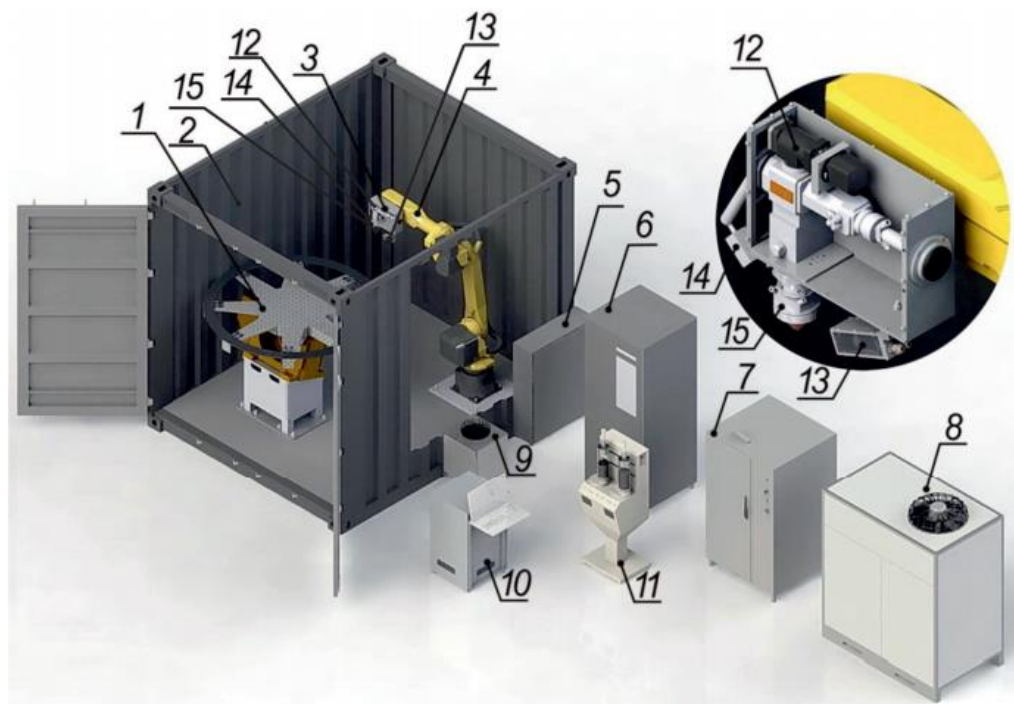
Загальна схема обладнання для реалізації технологій лазерного наплавлення: 1–Двох координатний стіл; 2–Робоча камера; 3–Лазерна голова; 4–робото технічний маніпулятор; 5– Вузол підготовки та подачі газової суміші; 6–пристрій очищення та сушіння газу; 7– Волоконний лазер; 8–Охолоджувач; 9–система охолодження; 10–Пульти управління; 11– Пристрій для подачі порошку; 12–Система управління; 13–Система відеоспостереження; 14– Система моніторингу площі обробки; 15–Насадка. [7]
